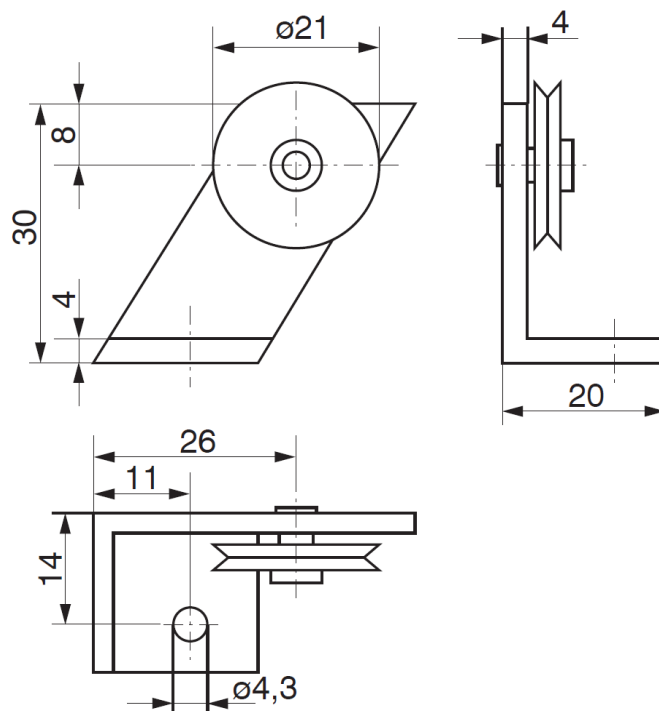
Magnetický držák MH1-WDS, rozměry jsou uvedeny v mm.
